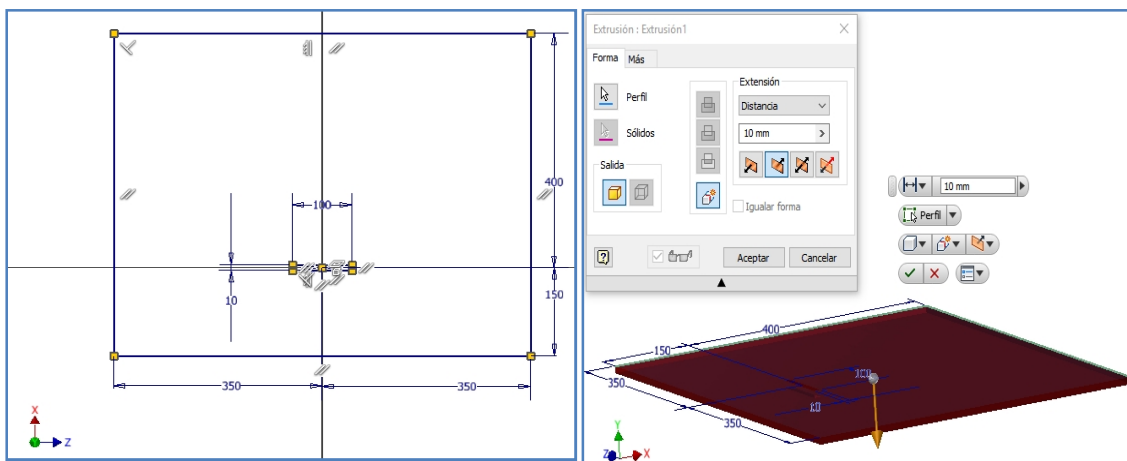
A. Boceto 1 para realizar la extrusión 1-Izquierda. Figura 4.7.B. Extrusión 1-Derecha.
